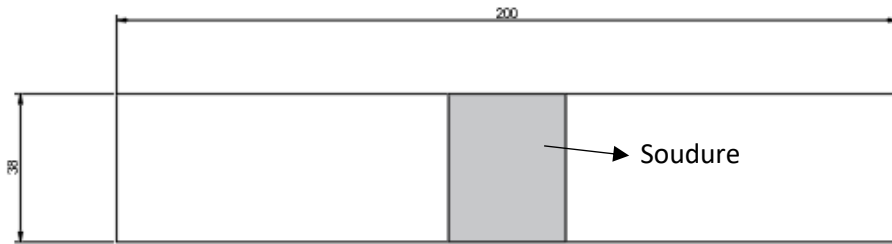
Éprouvette des essais de pliage selon la AWS D1-2 [44] (dimension en mm)
